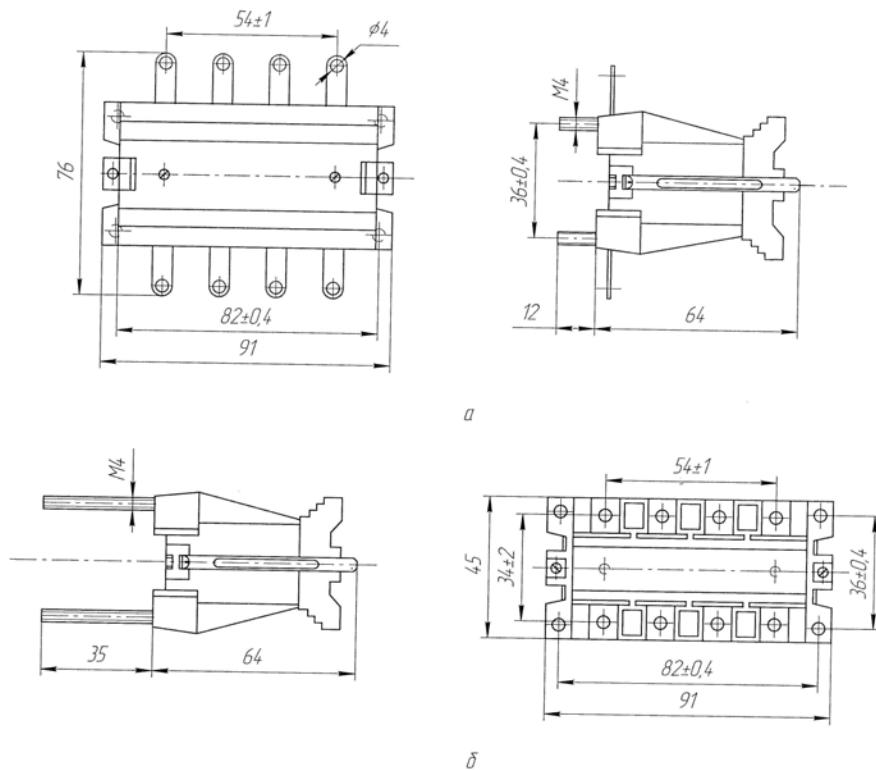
Габаритные, установочные и присоединительные размеры блока типа БИ 4М
